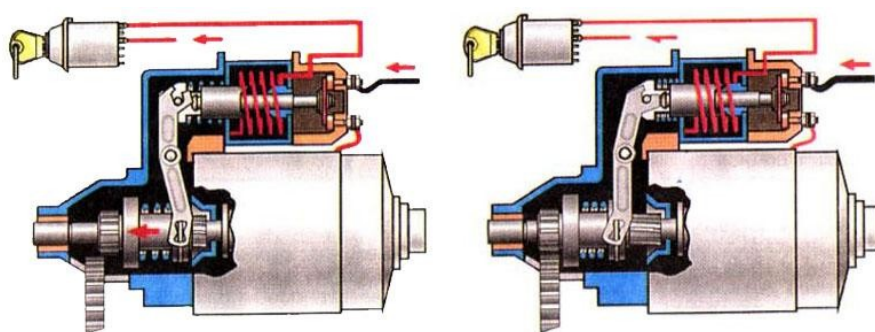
Зацепление шестерни привода с венцом маховика двигателя
